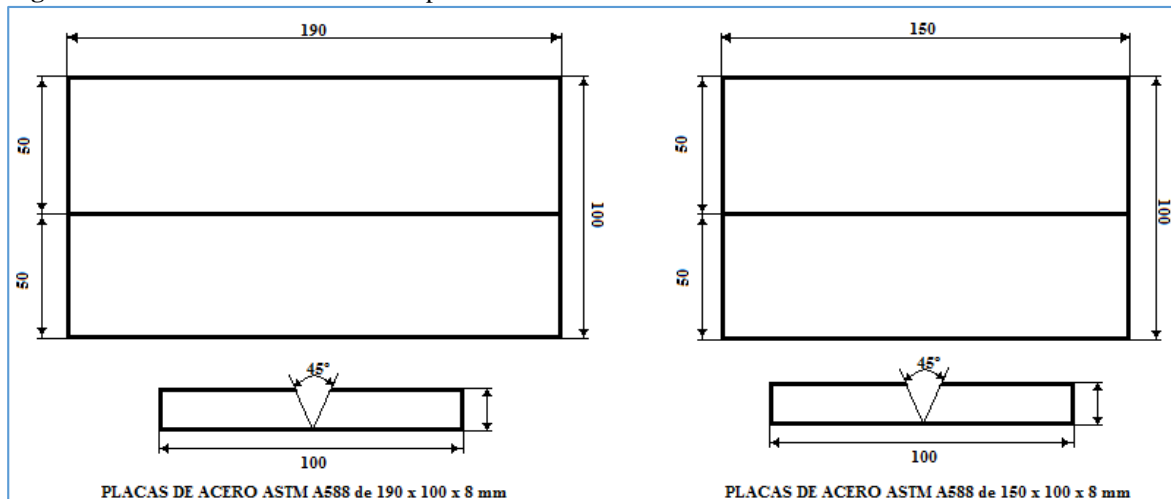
Simbología de soldadura típica unión a tope simple en V
